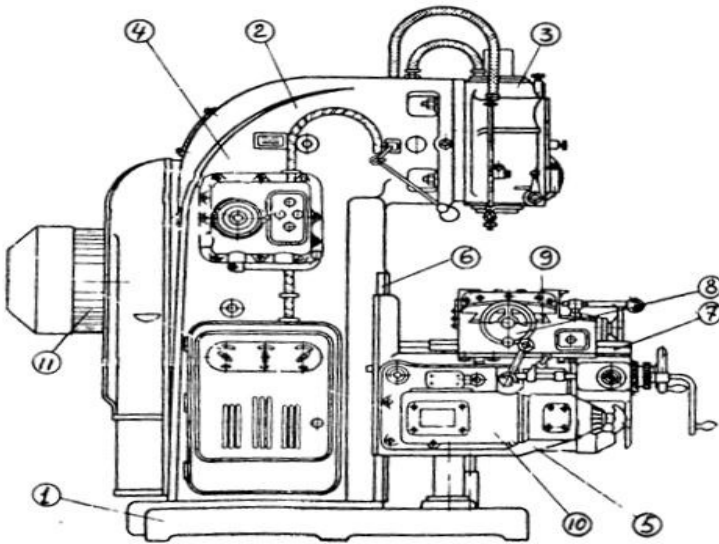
Загальний вигляд горизонтально-фрезерного верста-
